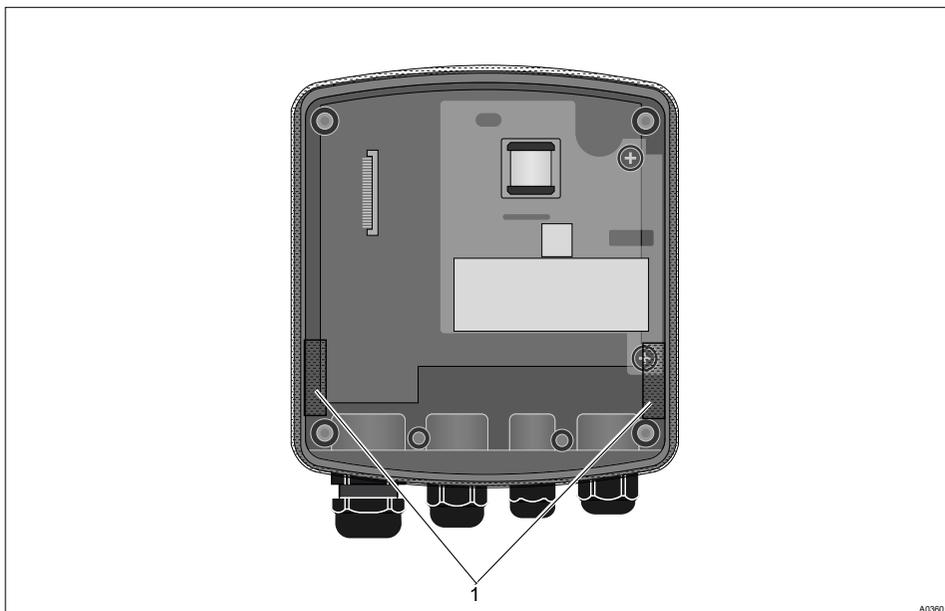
Установка профильного уплотнения на нижнюю часть корпуса регулятора
